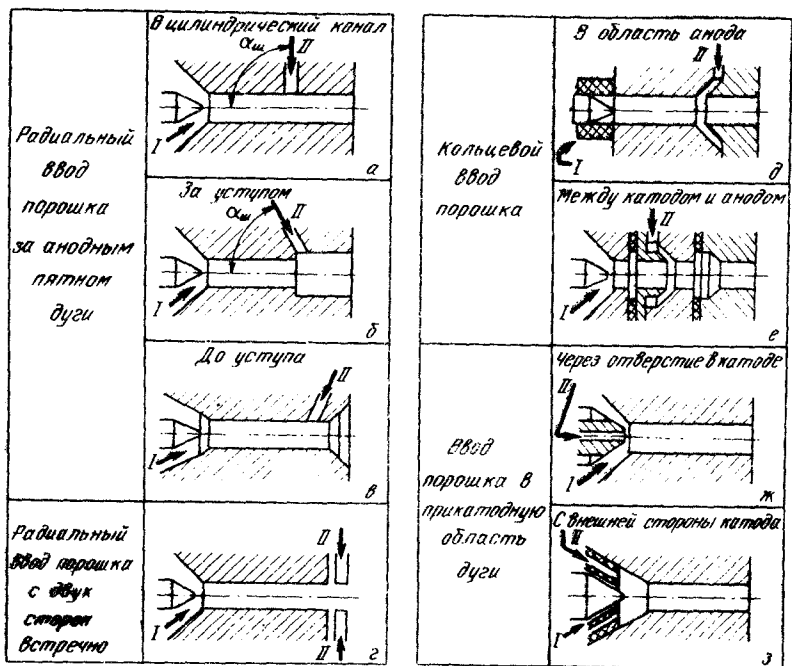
Схемы ввода порошка в плазменный распылитель:
